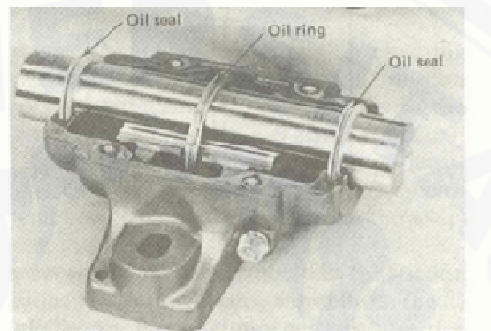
Macam – macam dari *bearing* (sumber : skf.com)
